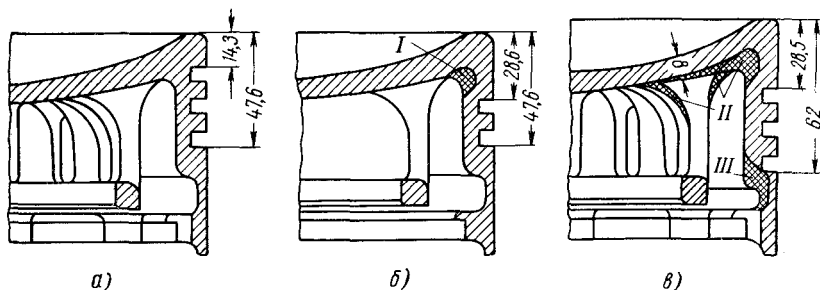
Поршни двигателя Фербенкс — Морзе:
